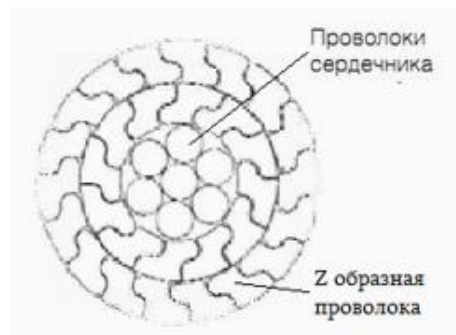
Поперечное сечение провода с Z образной проводящей проволокой
